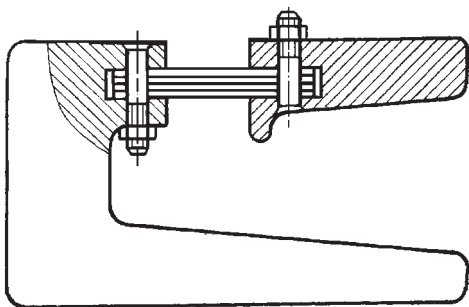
Регулируемая пружинная скоба (запорное устройство кокиля)
